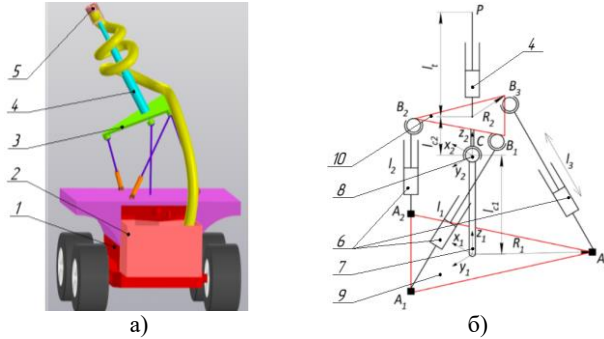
Схема РТС для сбора фруктов: а - 3D модель, б - расчётная схема платформы.
